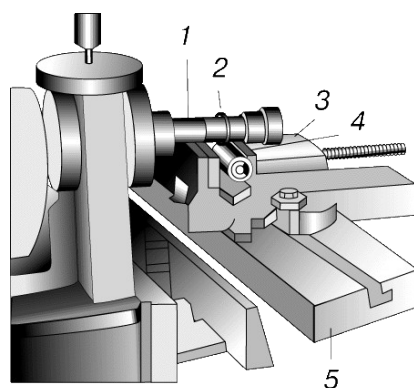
Схема горизонтально-фрезерного станка: 1 – оправка; 2 – фреза; 3 – тиски; 4 – деталь; 5 – стол
